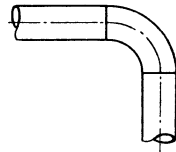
Einschweißbogen (Hamburger Rohrbogen).
